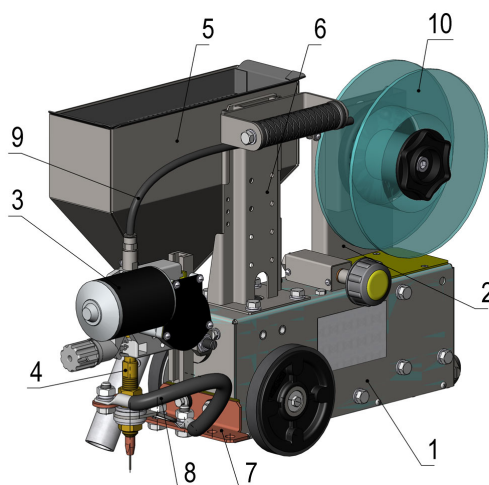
Основные части трактора (сварка под слоем флюса)
